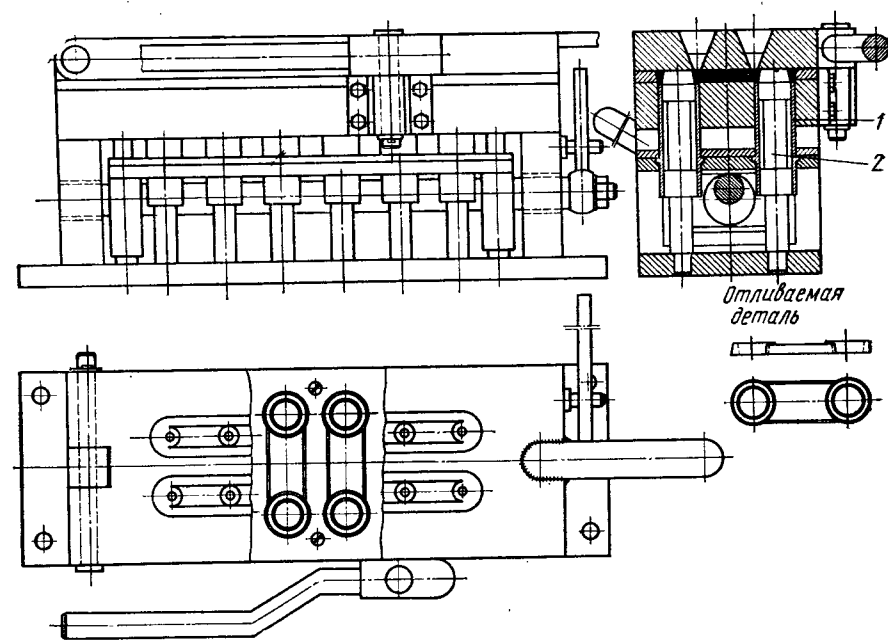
Малогабаритный станок для отливки межэлементных соединений
